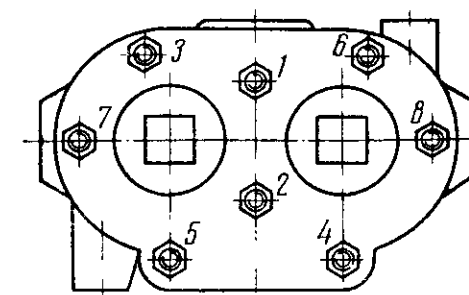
Последовательность затяжки гаек крепления головки блока компрессора.
